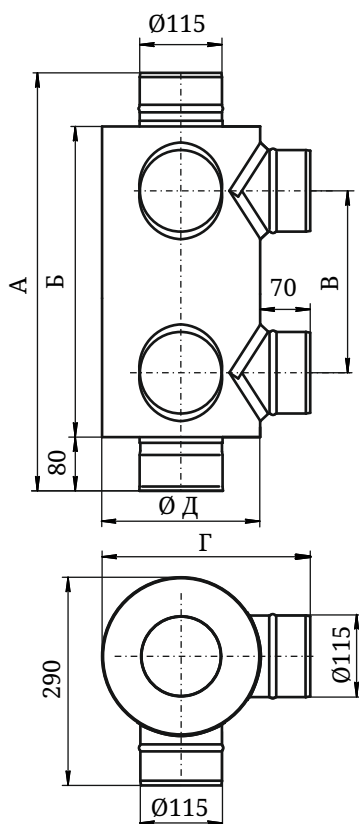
Отопитель натрубный для обогрева двух смежных помещений
